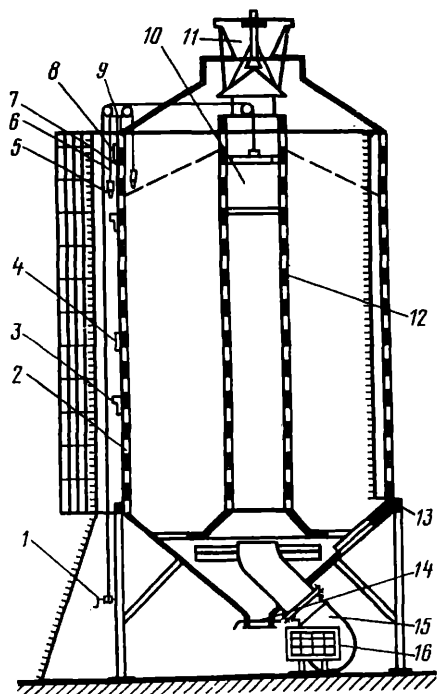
Вентилируемый бункер БВ-25: 1 — лебедка; 2 — корпус бункера; 3 — пробоотборник; 4 — регулятор влажности; 5, 7 — грузики; 6 — флажок фиксатора; 8 — датчик уровня зерна; 9 — кронштейн с блоками; 10 — цилиндрический поршень (клапан); 11 — конусный распределитель зерна; 12 — воздухораспределитель; 13 — регулировочное кольцо; 14 — заслонка; 15 — вентилятор; 16 — электрокалорифер.
